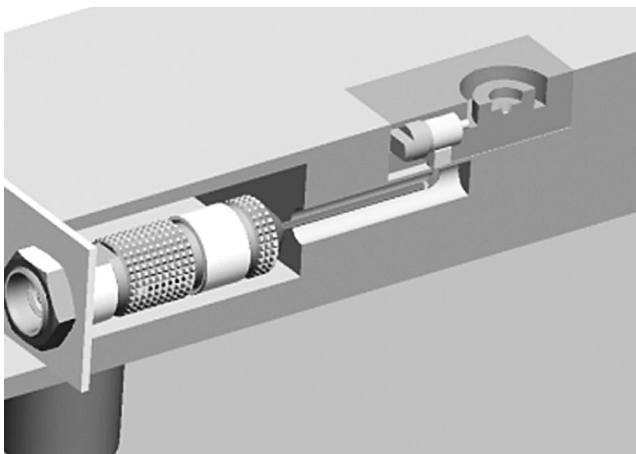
Seitlicher Einbau mit Sensor, Kabel, Stecker und Montageplatte
